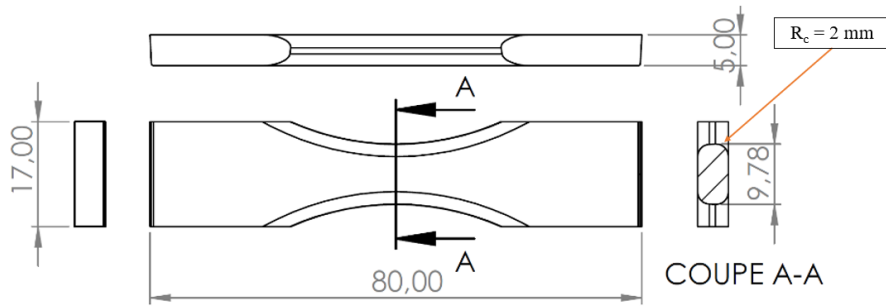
Géométrie d'une éprouvette test de 5 mm d'épaisseur, R_c = rayon de courbure
